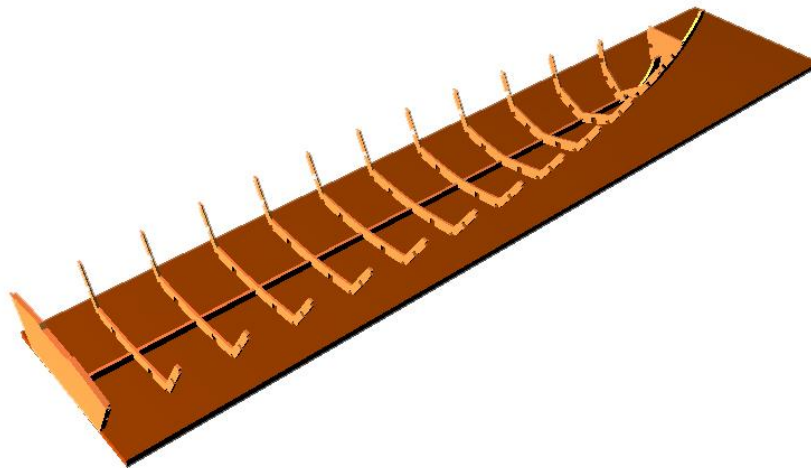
Imagen del encaje entre la quilla y las cuadernas
